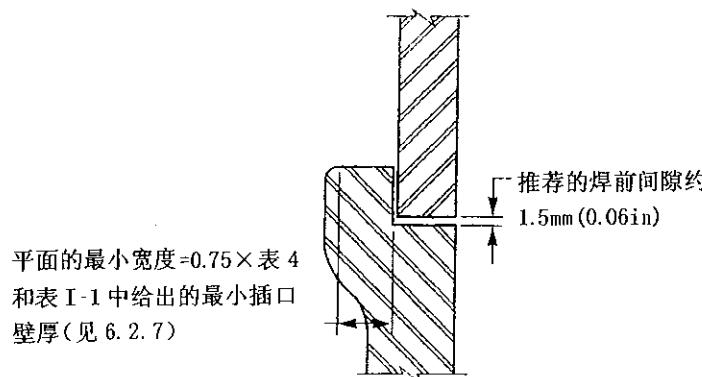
承插焊管配件所要求的焊接间隙和最小平面宽度尺寸
